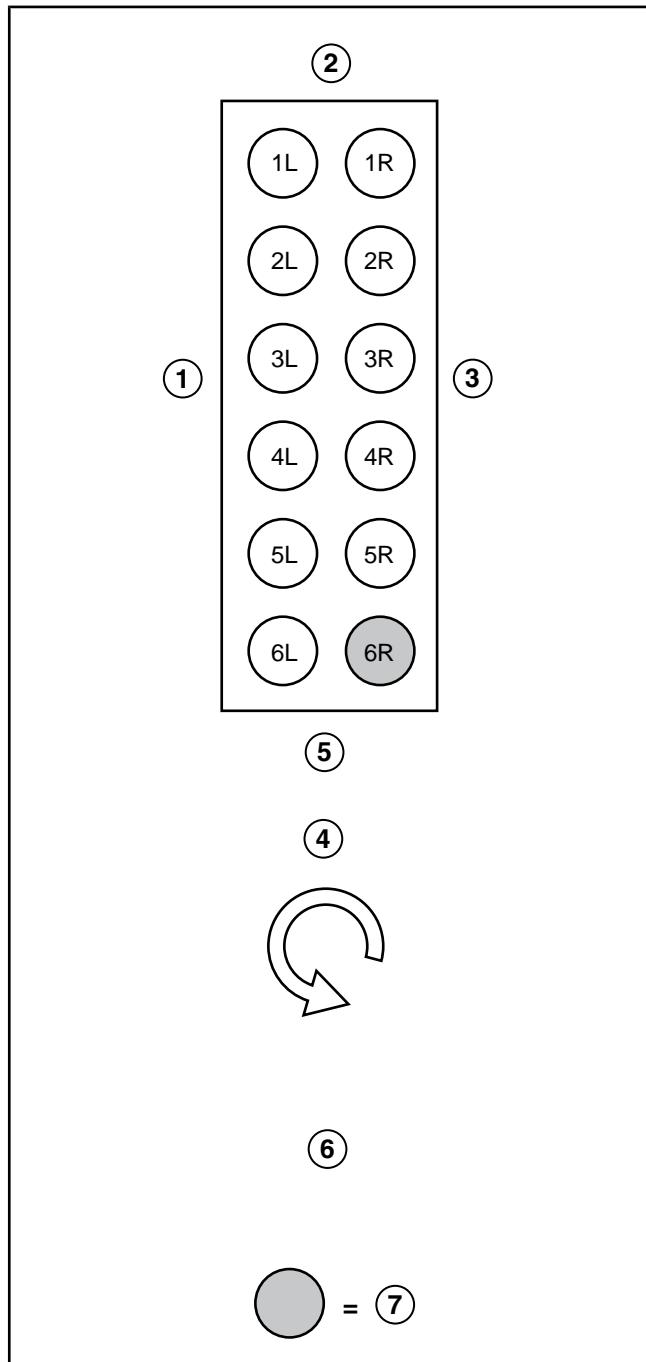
Порядок работы цилиндров двигателя и направление вращения вала
